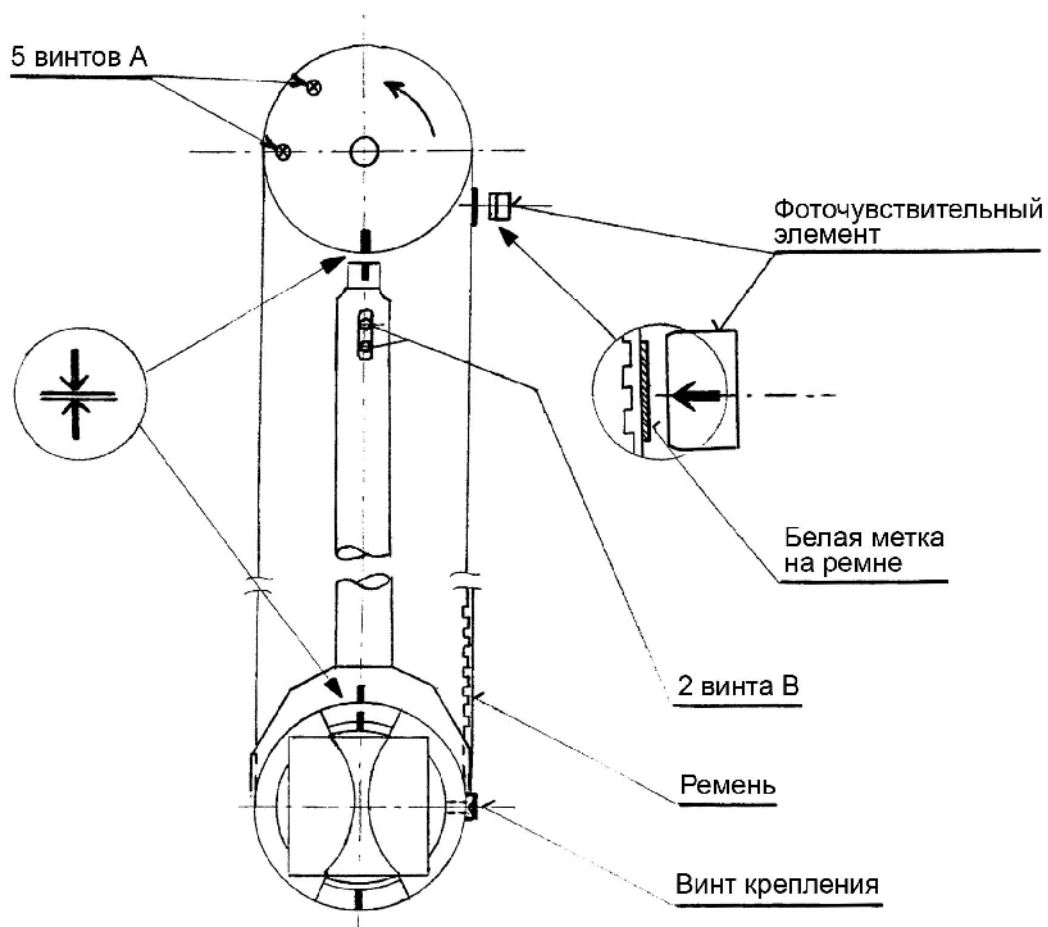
Модель МФК-1, регулировка ремня - версии FA и A
